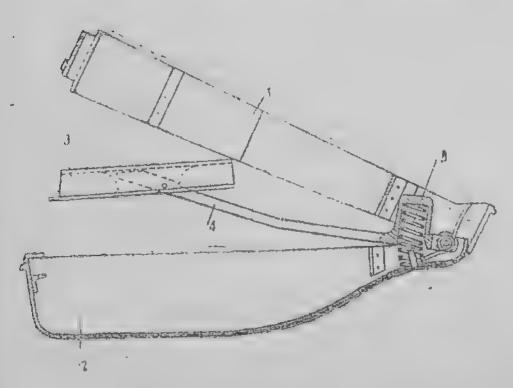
Магазин: 1-керобка; 2крышка; 3-подаватель; 4-рычаг; 5-пружина рычага подавателя
